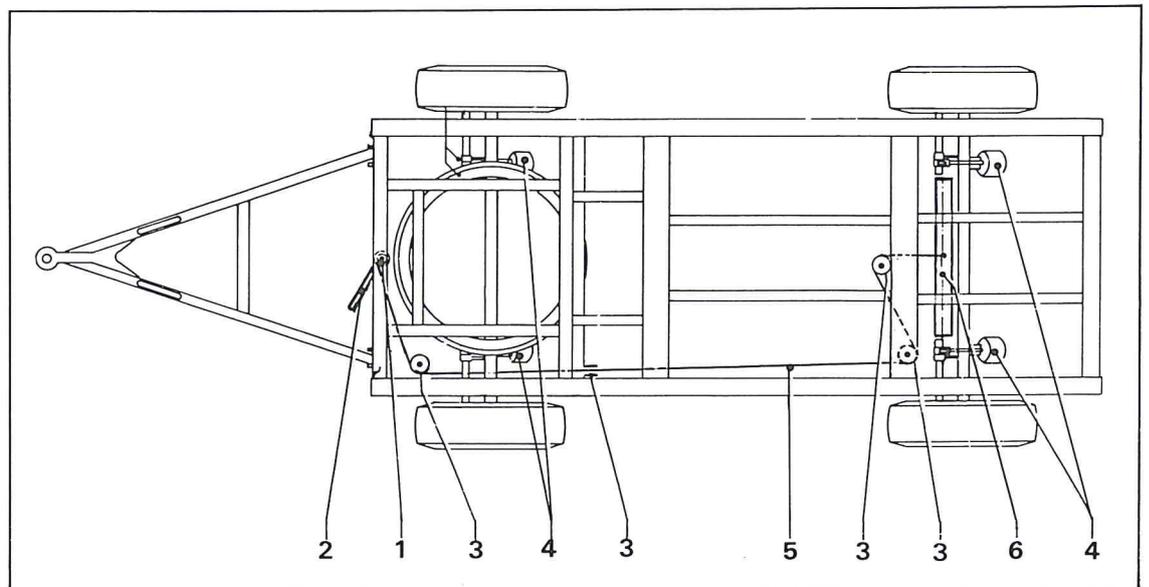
Stellbremsanlage für Aggregat-Anhänger
